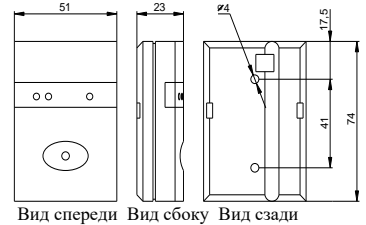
Внешний вид, габаритные и установочные размеры корпуса извещателя
